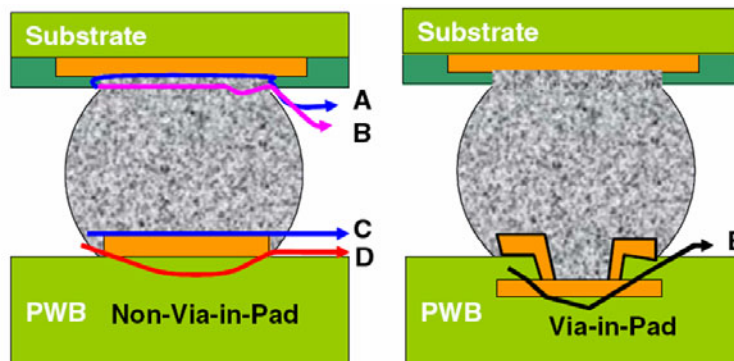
Principaux modes de rupture des joints de soudure, schéma de principe théorique [12].
